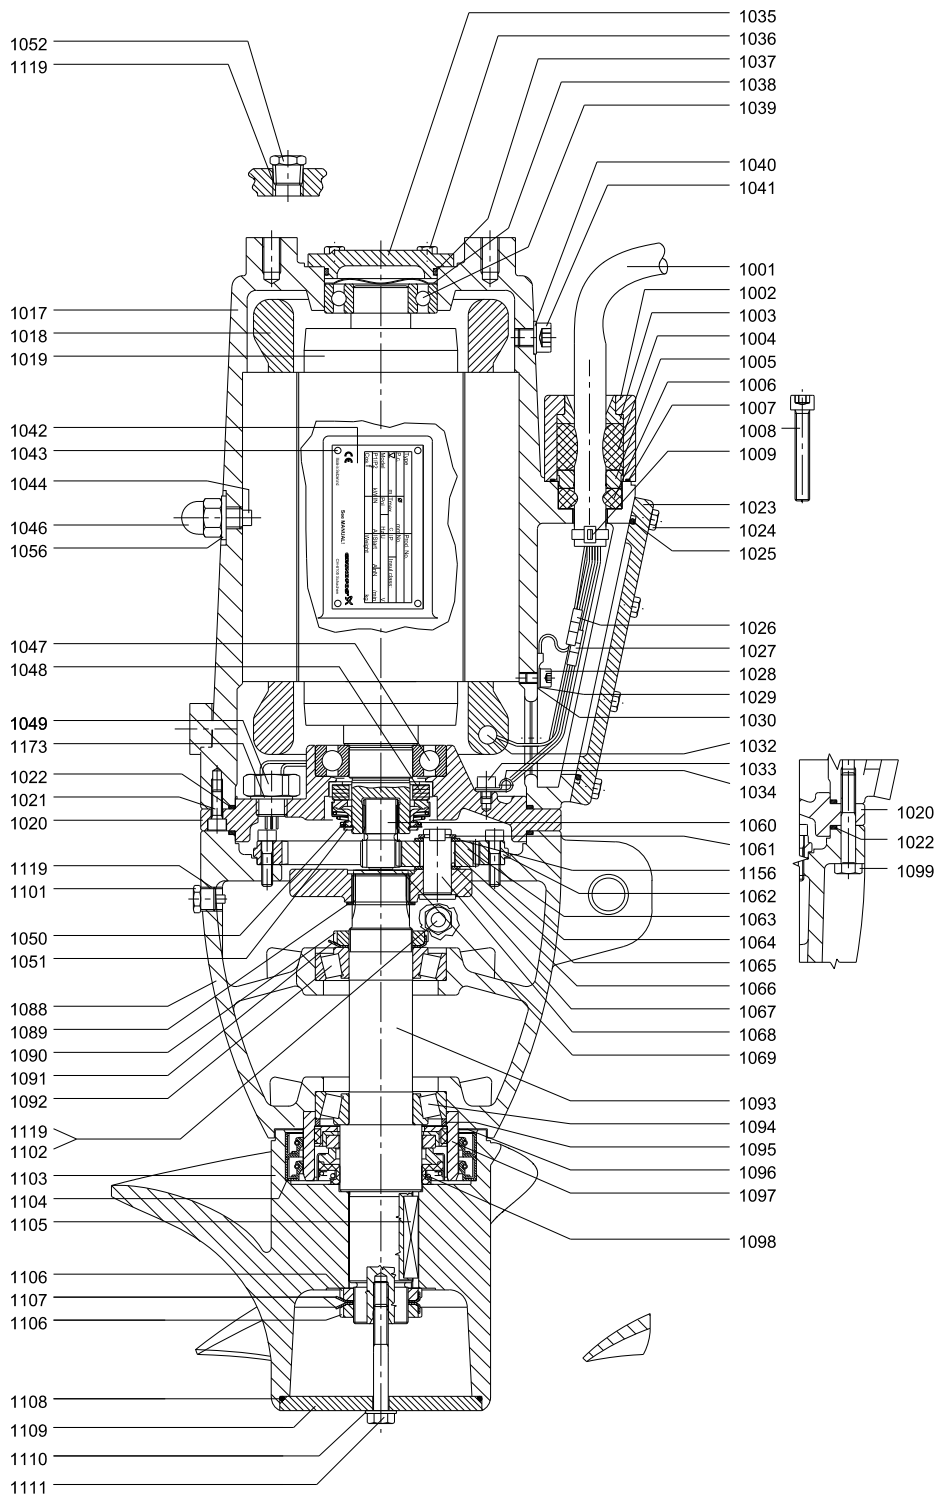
Чертёж в разрезе, SRP.xx.30.xxx
